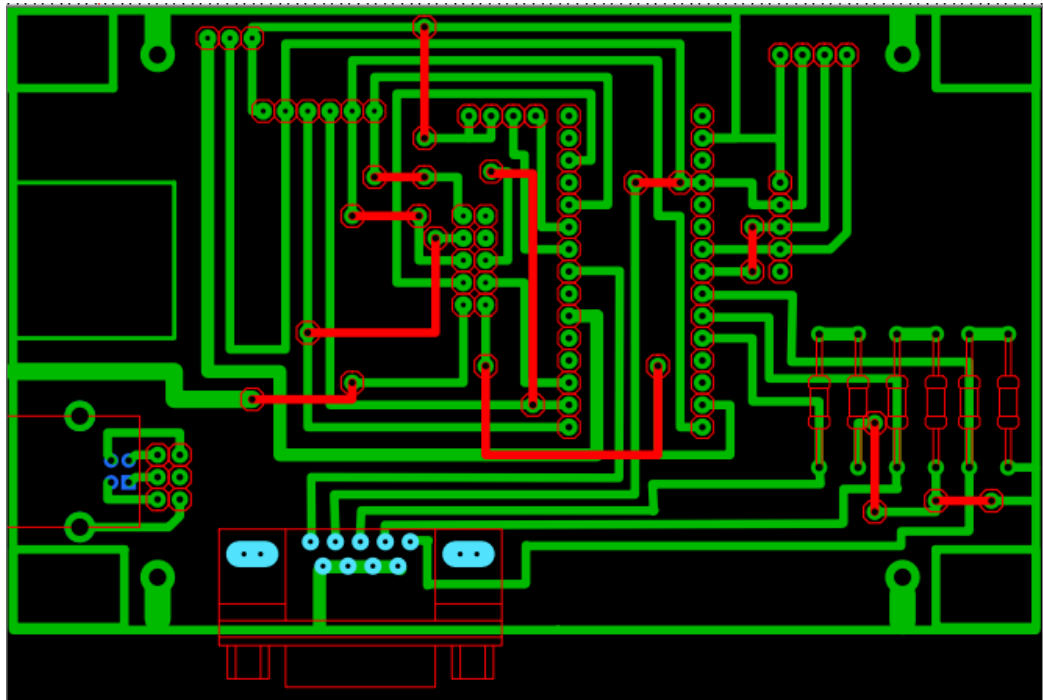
Вигляд плати в Sprint-Layout
